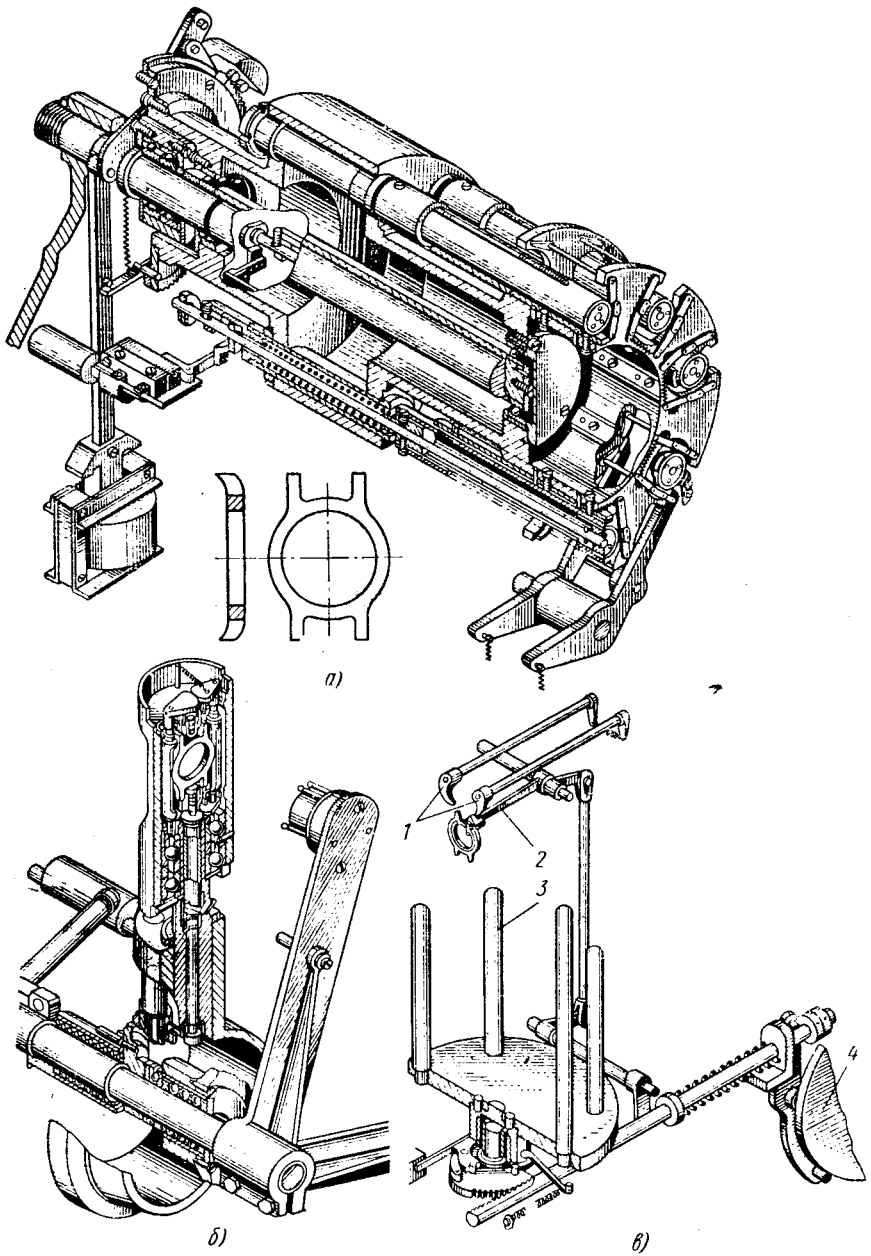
Механизмы автоматической линии для обработки корпуса наручных часов:
